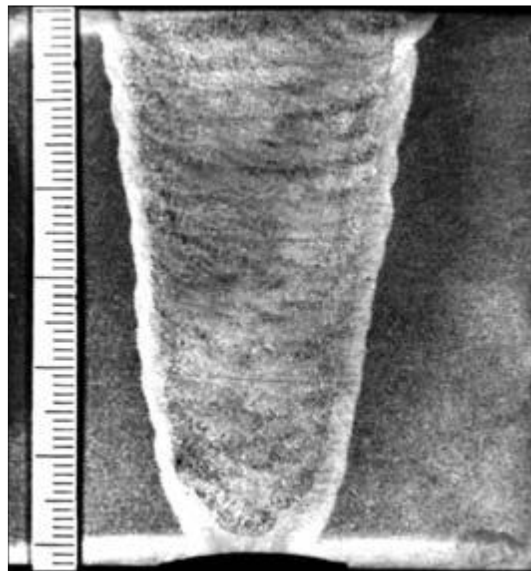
Макроструктура контрольного сварного соединения
